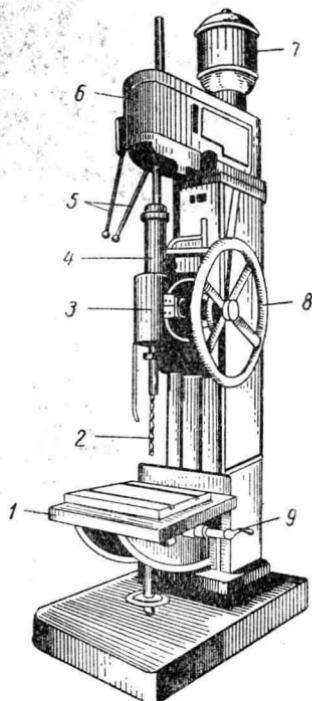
Одношпиндельный вертикально-сверлильный станок типа 2150:
